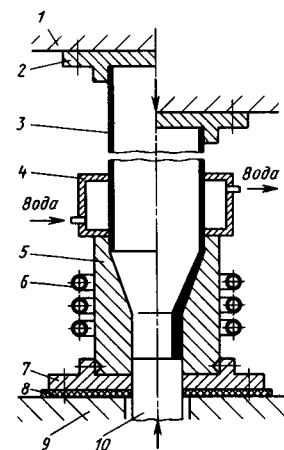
Схема штампа для обжима труб с нагревом: 1 — траверса прессы; 2 — направляющая трубы; 3 — трубчатая заготовка; 4 — охладитель; 5 — матрица; 6 — индуктор ТВЧ; 7 — опора; 8 — теплоизолятор; 9 — стол прессы; 10 — выталкиватель
